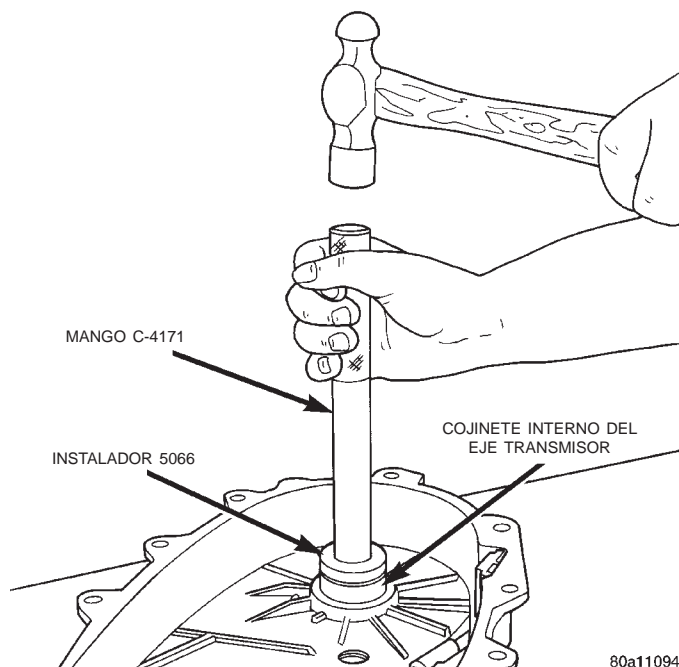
Instalación del cojinete trasero del eje transmisor delantero
